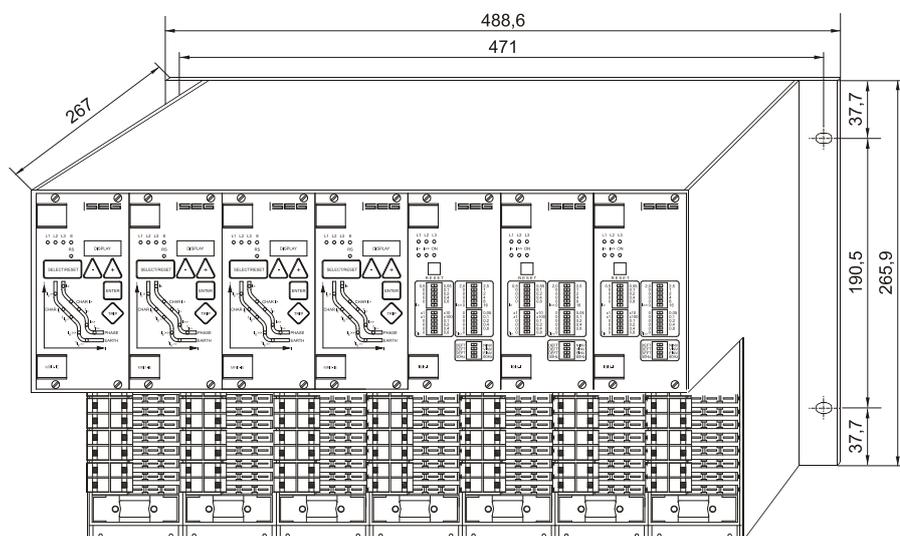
Baugruppenträger für Montageplattenaufbau mit Relaisvariante A, 84 TE
